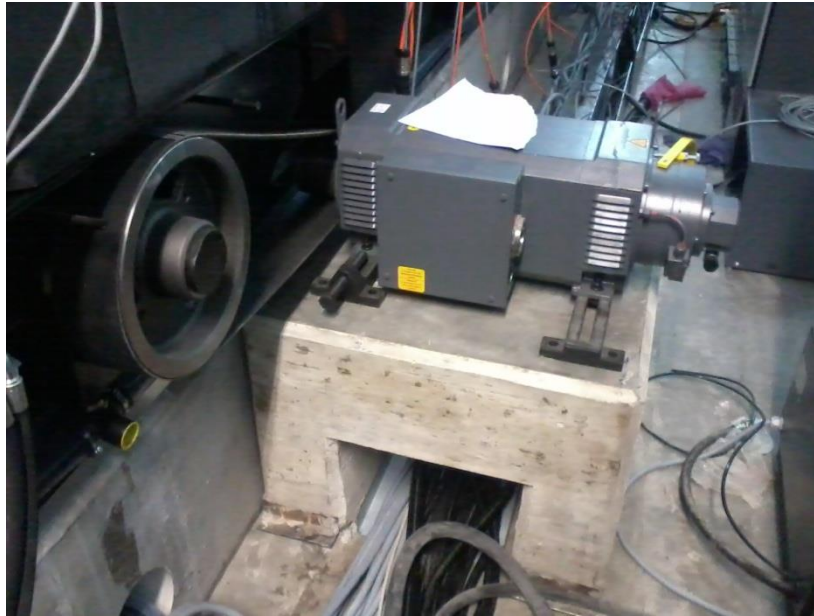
Motor principal elevado con el cubo de concreto.
